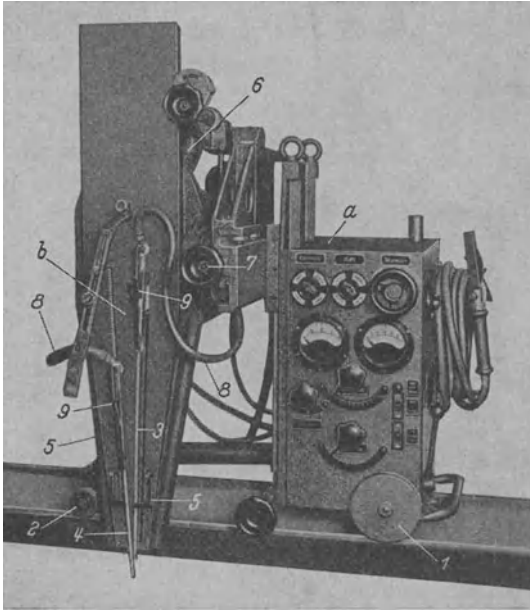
Halbselbsttätige Schweißeinrichtung für Stabelektroden.
